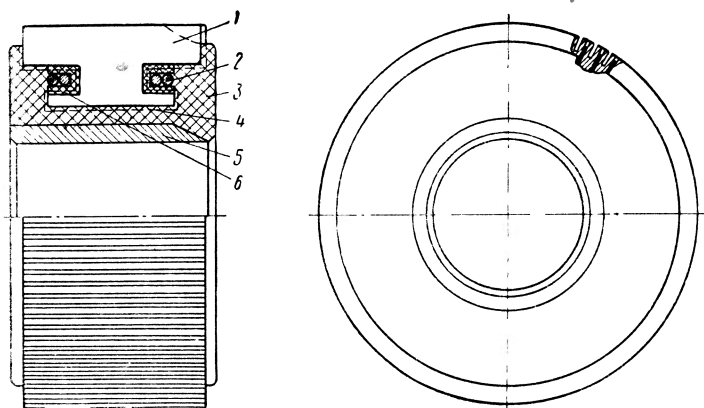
Цилиндрический коллектор с креплением пластин пластмассой:
